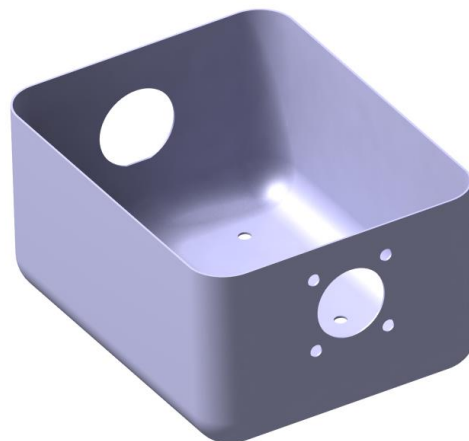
Příklady součástí vyrobených technologií tažení [3], [4], [5], [6]
